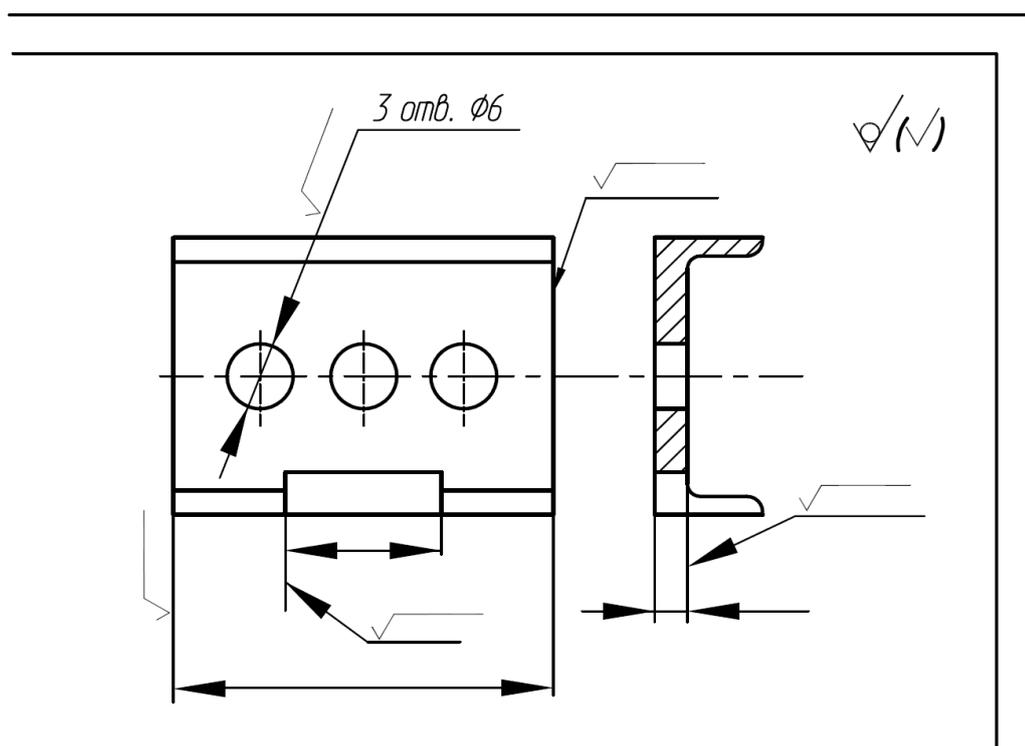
Обозначение шероховатости поверхностей, которые не обрабатываются на данном чертеже
